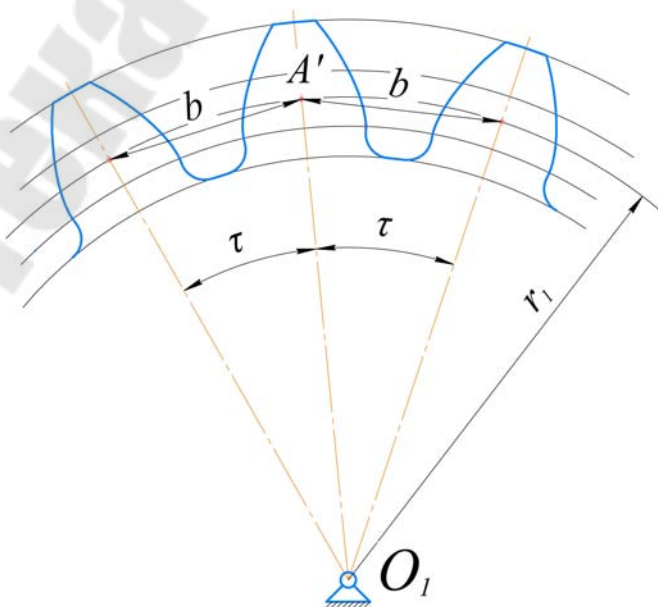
Построение второго и третьего зуба зубчатого колеса
